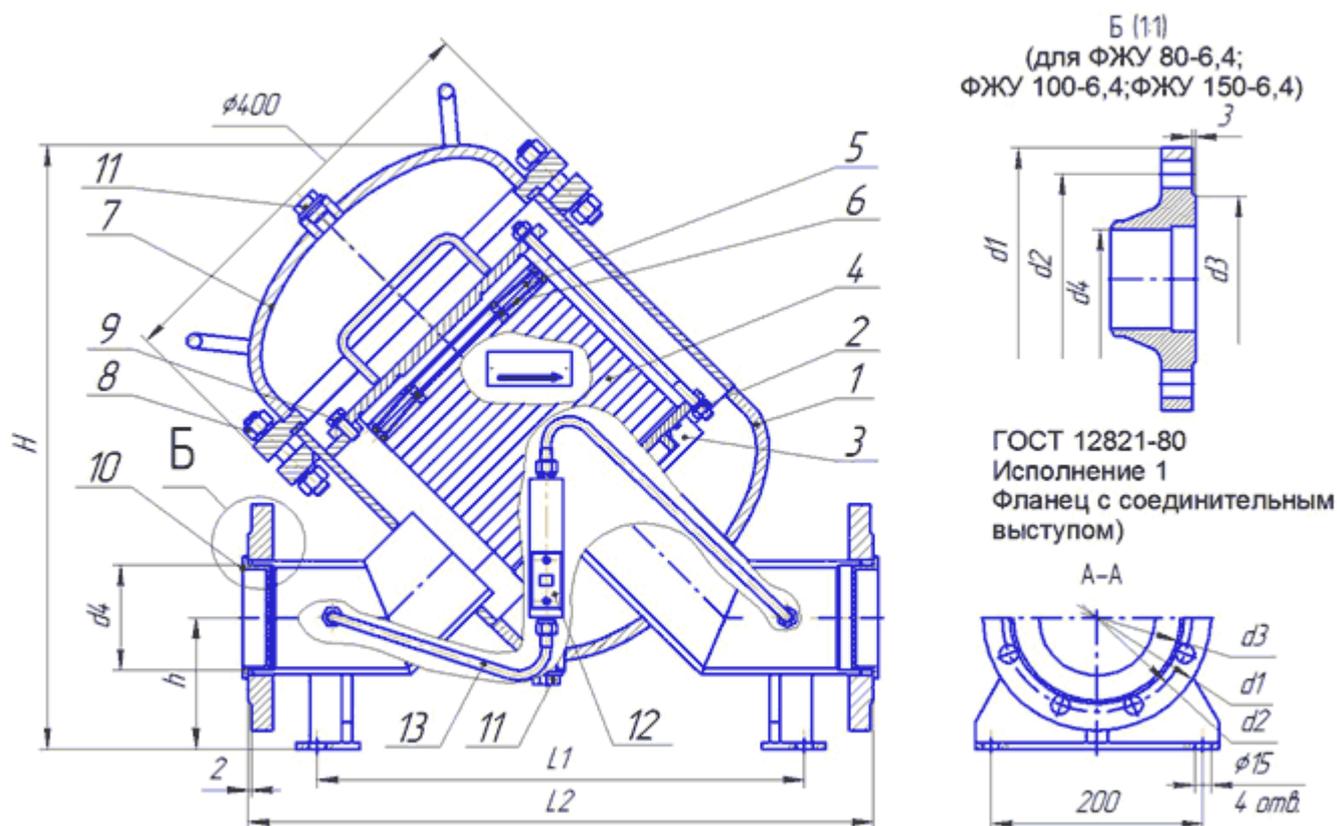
Фильтры жидкости ФЖУ 80-1,6; 80-6,4; 100-1,6; 100-6,4; 150-1,6; 150-6,4. Габаритные и присоединительные размеры.. (1 - корпус; 2, 8 - гайки; 3 - основание; 4 - фильтрующий элемент; 5 - сетка; 6 - диск; 7 - крышка; 9 - болт; 10 - заглушка; 11- пробка, 12-индикатор перепада давления, 13-соединение).
